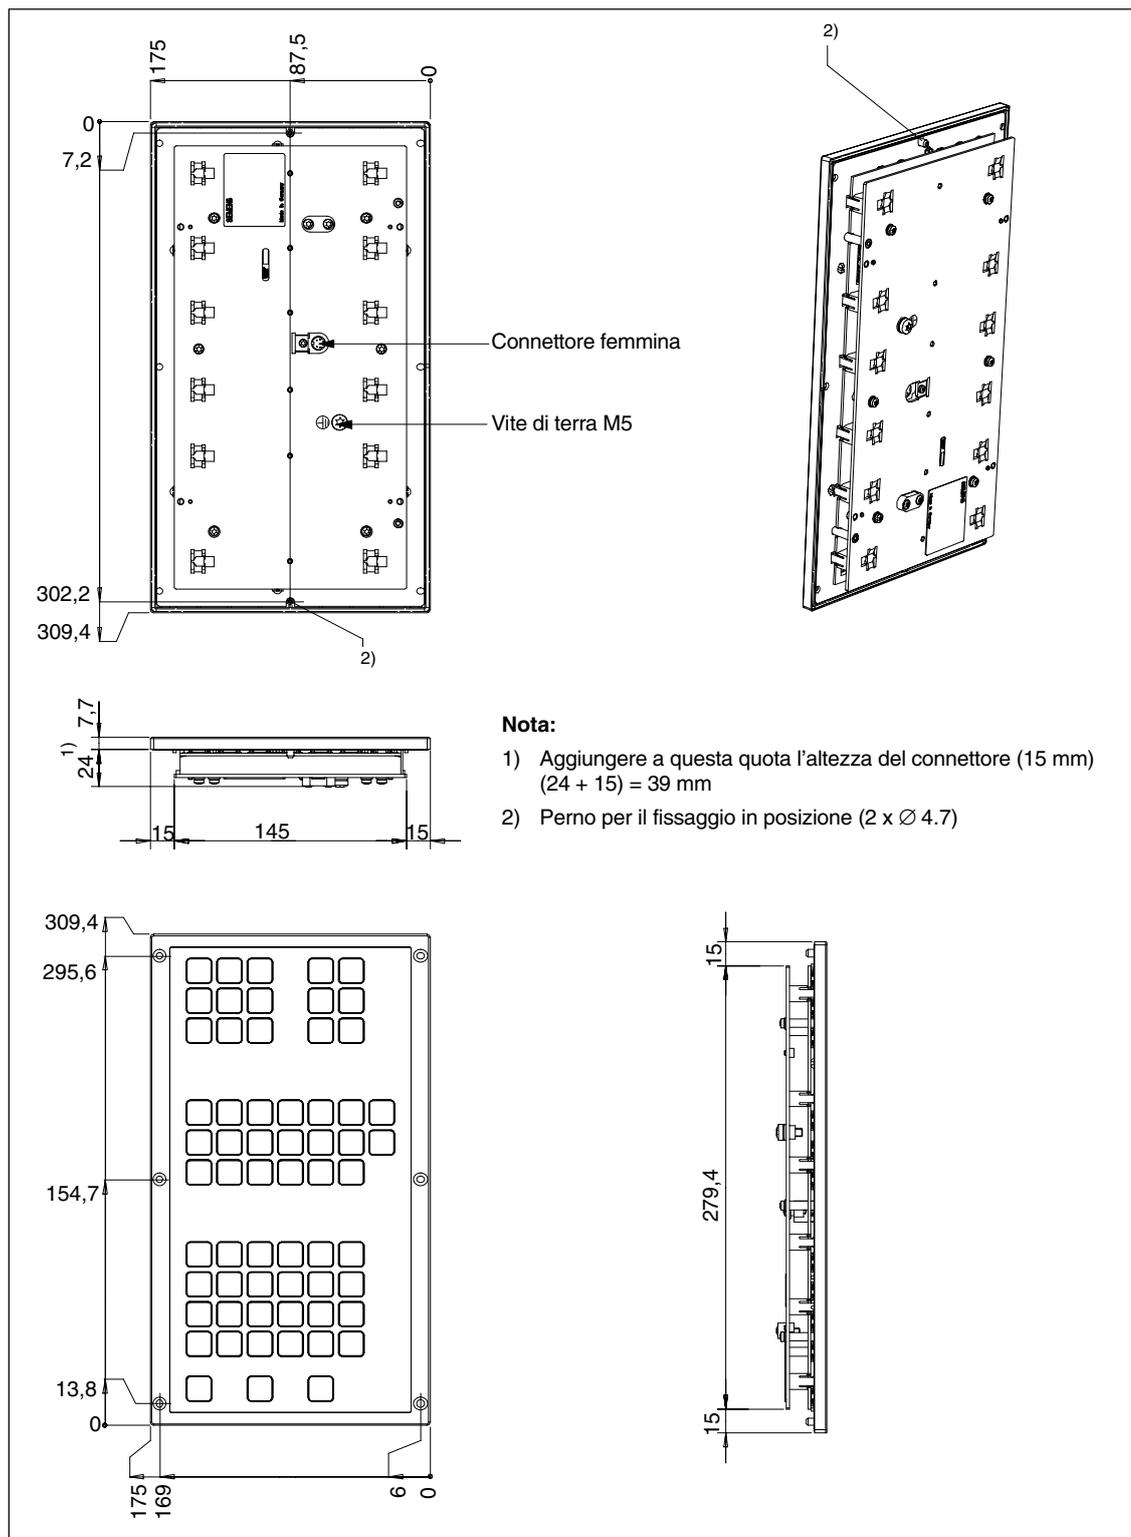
Disegno quotato della tastiera CN (montaggio sotto la PCU)
